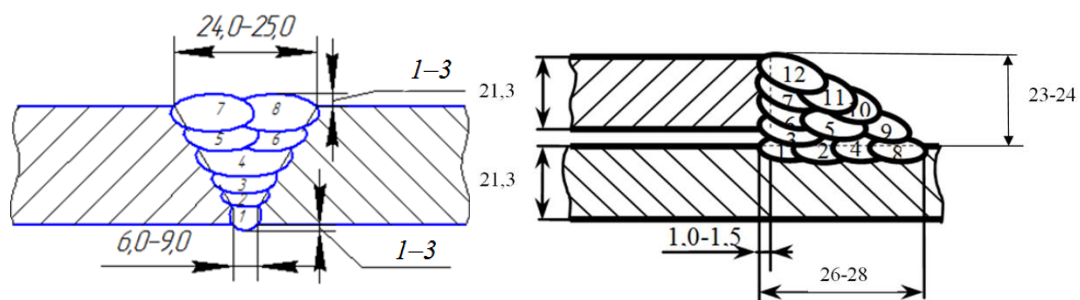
Конструкция стыкового и нахлесточного сварного соединения при подводной ручной и механизированной сварке [2]
